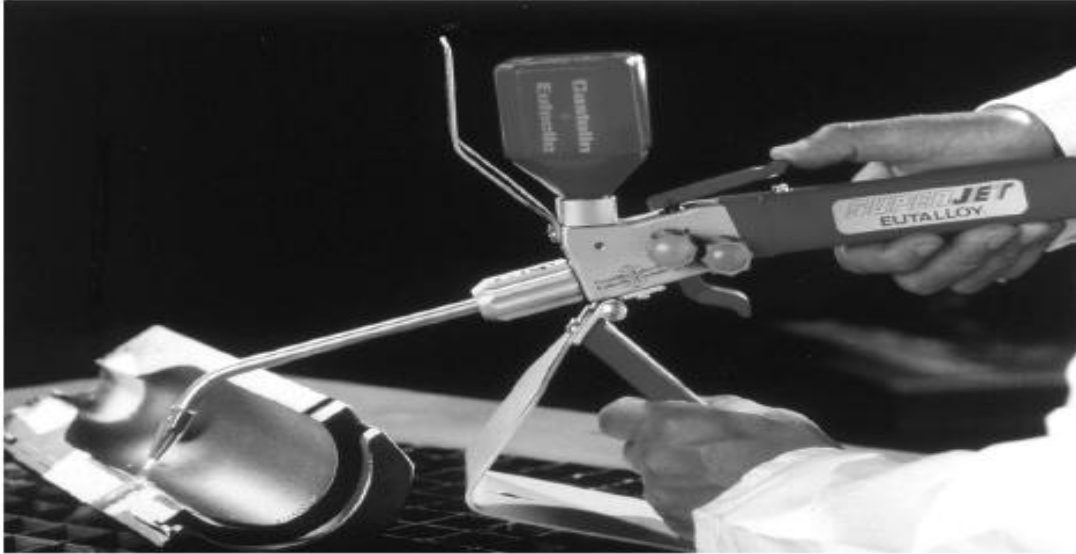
Projection flamme-poudre sur moule de verrerie (doc. Castolin) [24].
